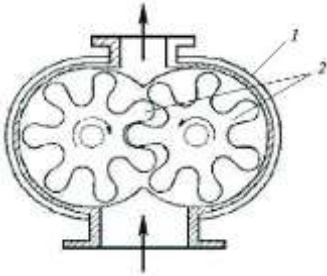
Схема шестерного насоса: 1 – корпус; 2 – шестерні
